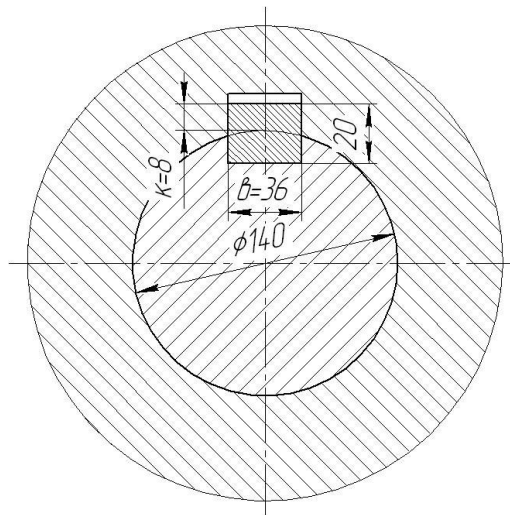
Шпонкові з'єднання вала лебідки
